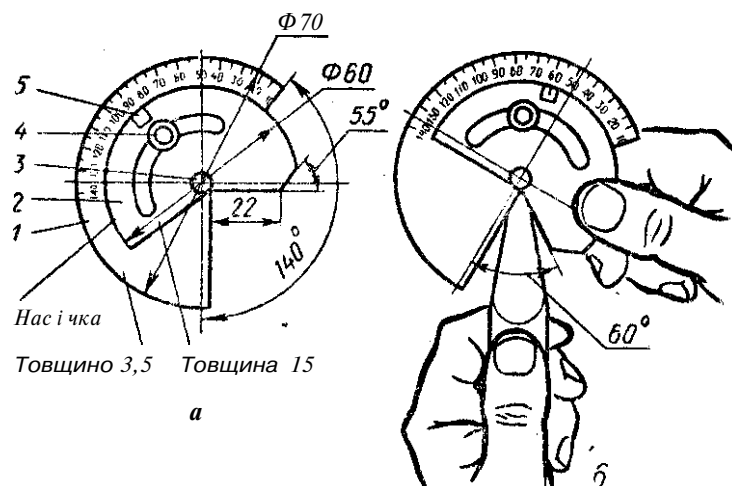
Прилад для перевірки елементів різальних інструментів; а — будова; б — прийом вимірювання
